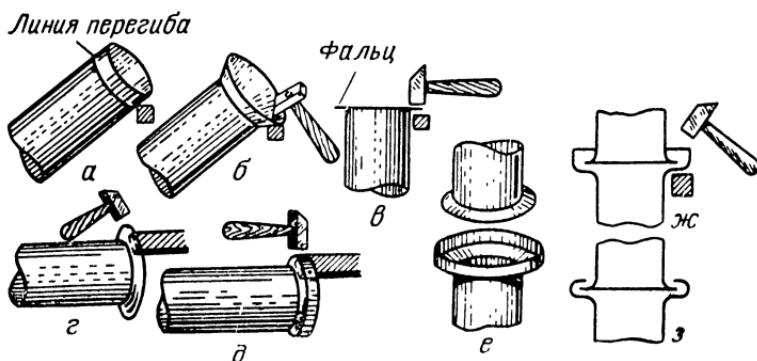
Последовательность изготовления стоячего фальцевого шва на цилиндрических изделиях:
